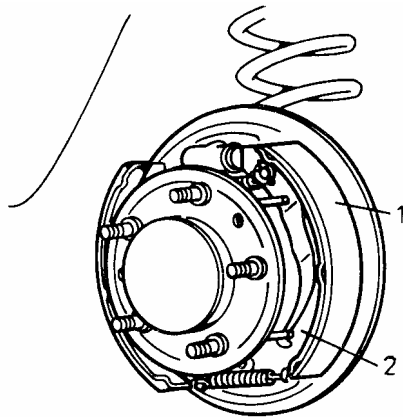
Freno trasero con tambor desmontado: 1 - forro de fricción; 2- zapata de freno
